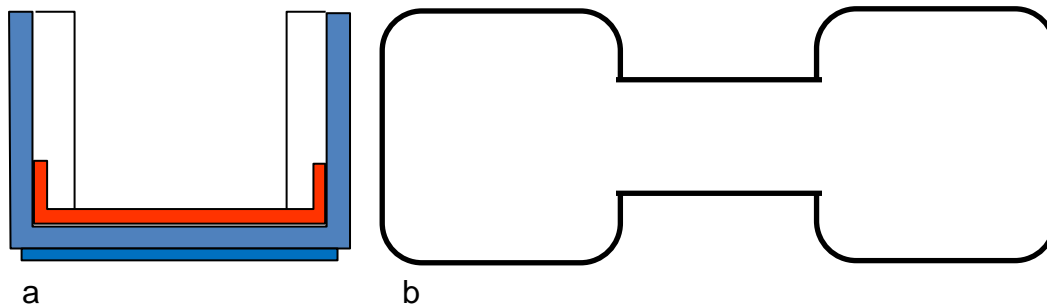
a) Schnitt A-A im Bild 4.15b, b) Halbzeug für das Polblech
